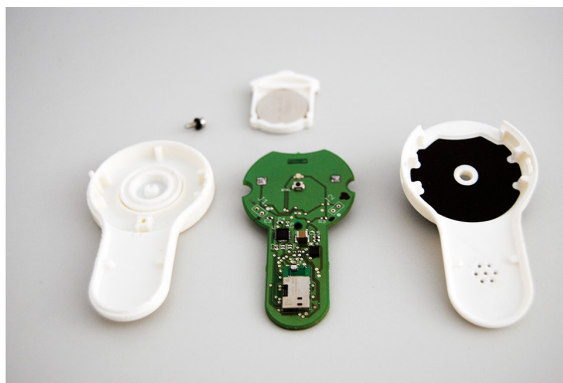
Protótipo final para teste do sensor; corpo superior e inferior, suporte da bateria, pilha e placa de circuitos impressos.
